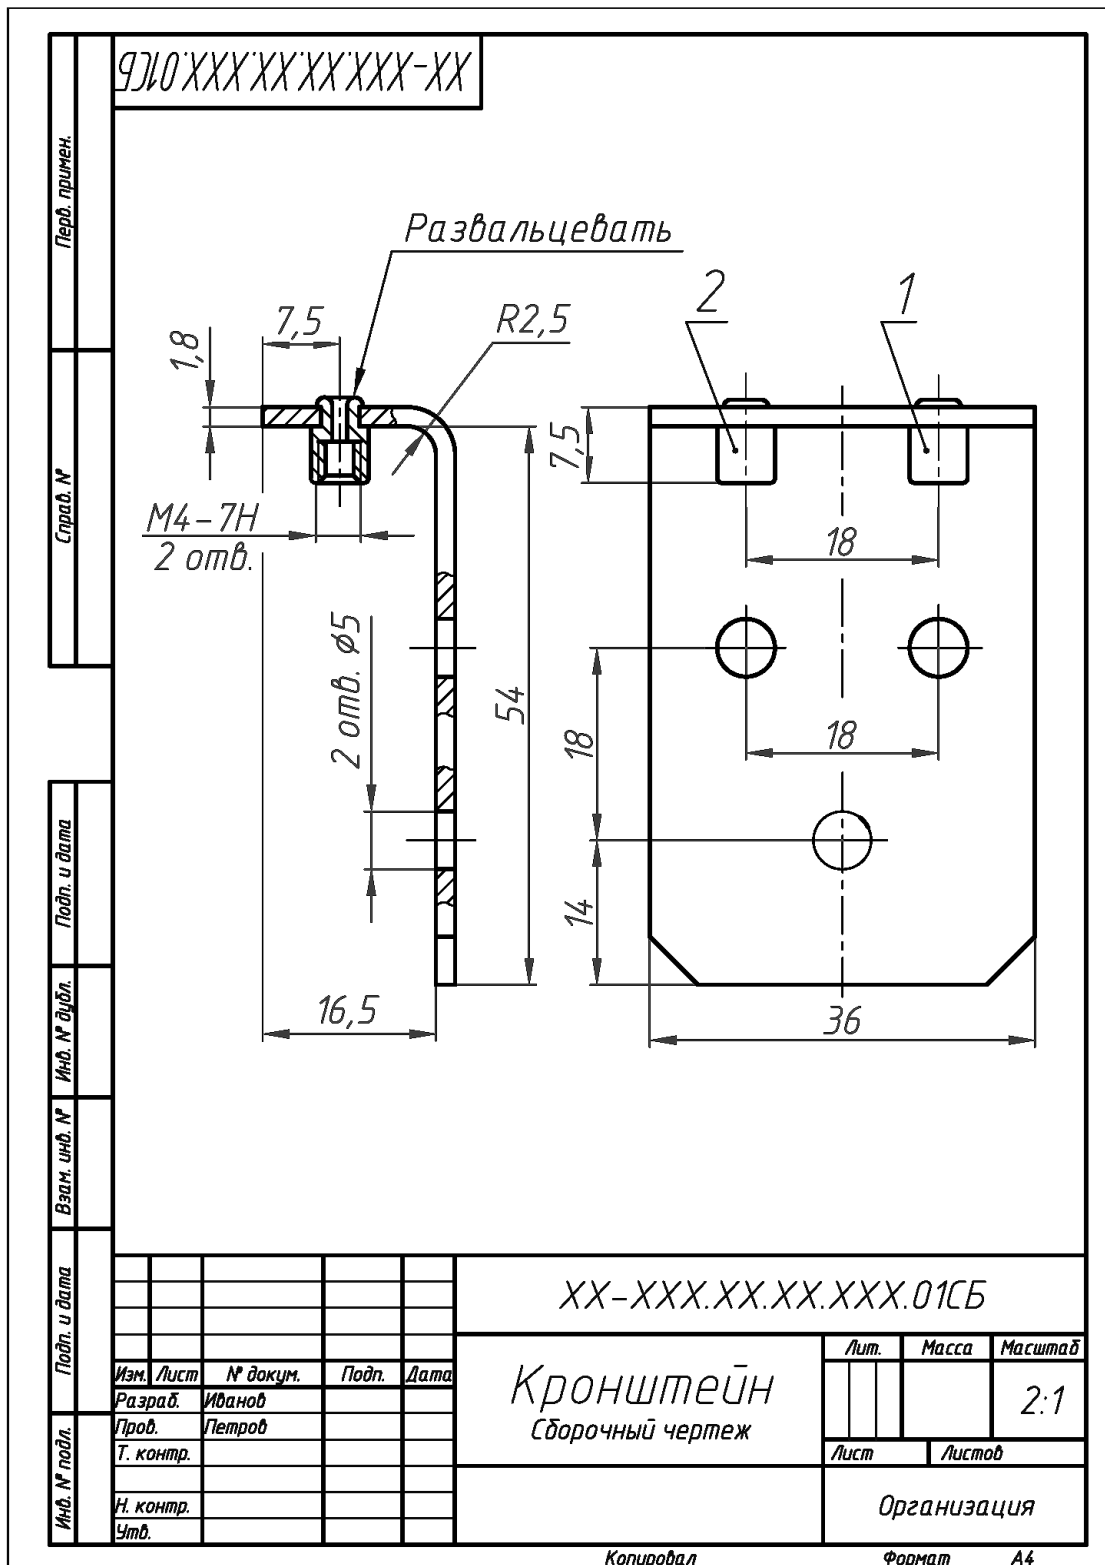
Пример выполнения и оформления сборочного чертежа изделия «Кронштейн» с цапфой в форме втулки
